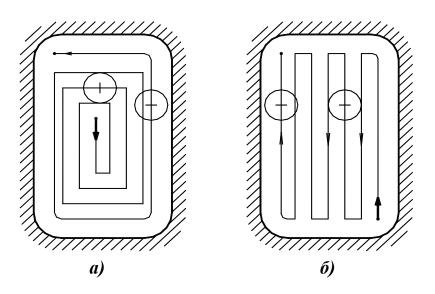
Траектория движения фрезы при формировании карманов: a) черновая обработка; δ) чистовая обработка
